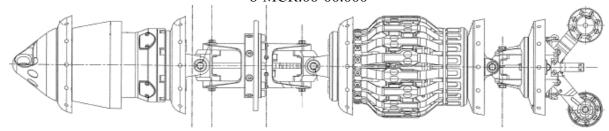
Чертеж общего вида дефектоскопа внутритрубного магнитного 6-MCK.01-00.000-01
